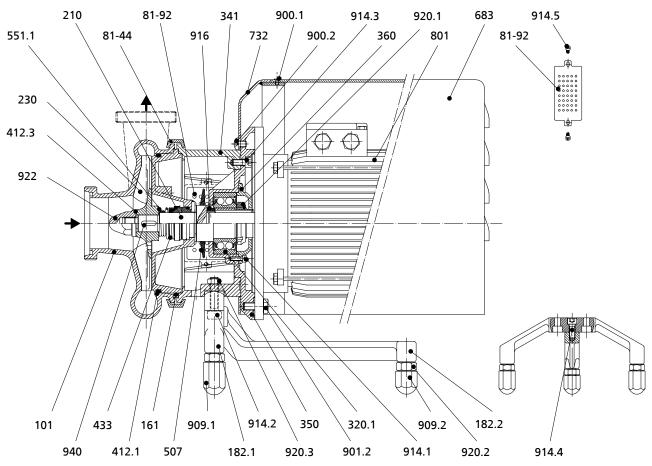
Сборочный чертеж, типоразмер двигателя IEC 71-112
